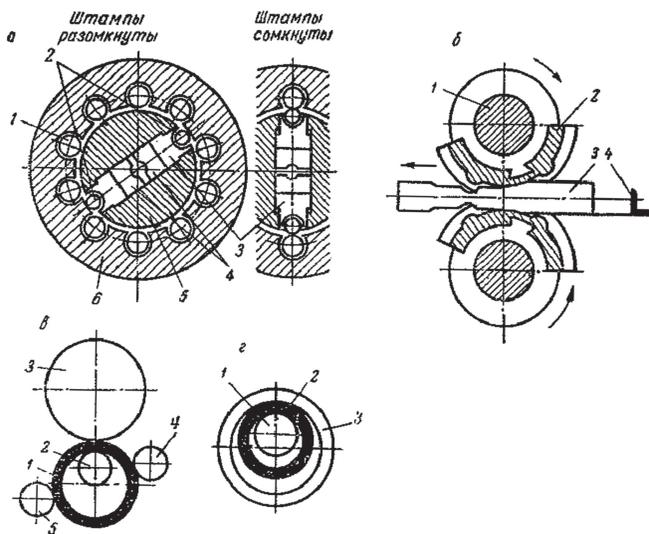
Ротационная ковка (а): 1 – нажимные ролики; 2 – ролики ползунов; 3 – ползуны; 4 – штампы (бойки); 5 – шпиндель; б – кольцевая обойма, вальцовка (б): 1 – валки; 2 – секторные штампы; 3 – заготовка; 4 – упор, раскатка: в – открытая, г – закрытая: 1 – заготовка; 2 – профилирующий ролик; 3 – матрица; 4 – направляющий ролик
